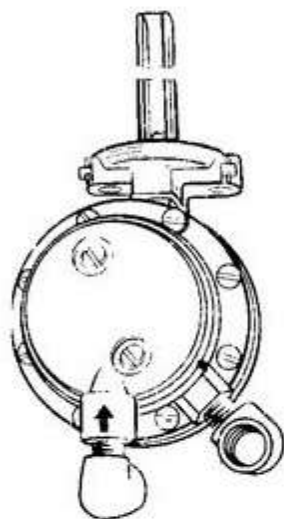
Положение штуцеров головки и крышки относительно корпуса насоса
